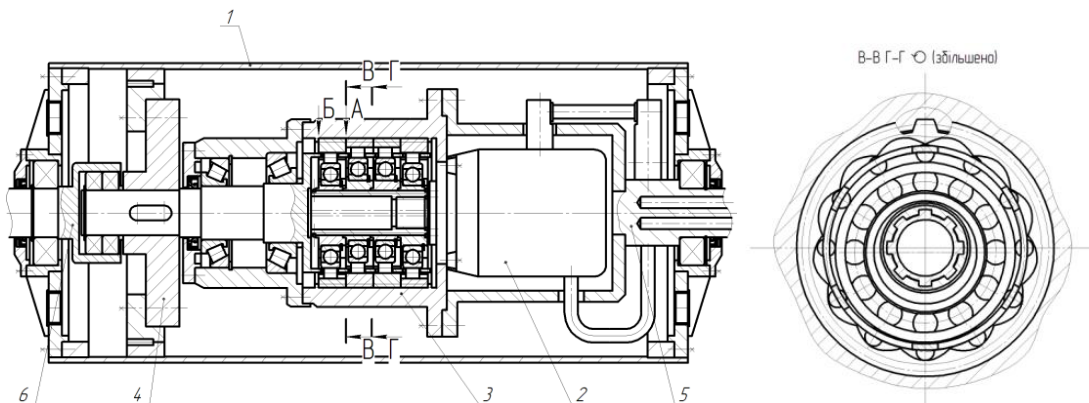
Конструктивна схема вмонтованого гідравлічного приводу фрезерного барабана
